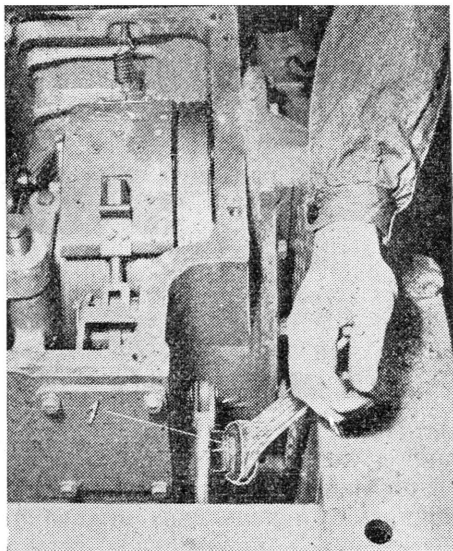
Регулировка механизма управления муфтой поворота при помощи корончатой гайки:
